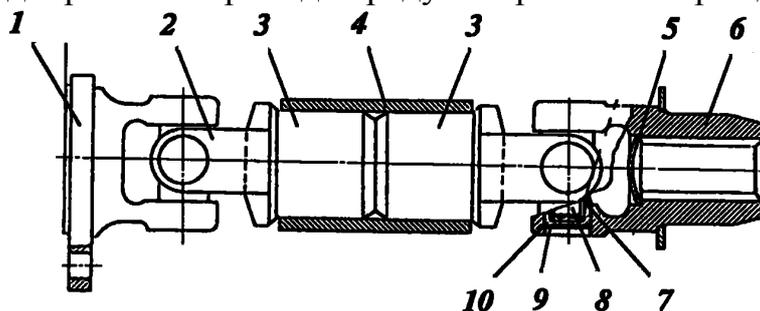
Привод: 1 - фланец; 2 - шарнир карданный; 3, 6 - вилки; 4 - труба; 5 - заглушка; 7 - обойма; 8 - крестовина; 9 - кольцо; 10 - подшипник
